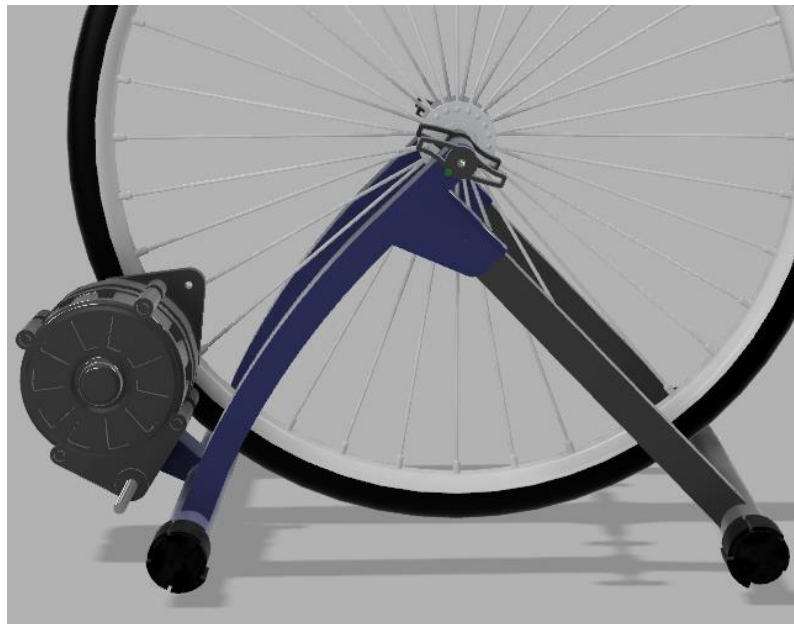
Gerendertes CAD-Modell des Rollentrainers mit M10-Gewindestange, angelegter Lichtmaschine und 28-Zoll-Fahrradreifen zur Prüfung des Schwenkradius
